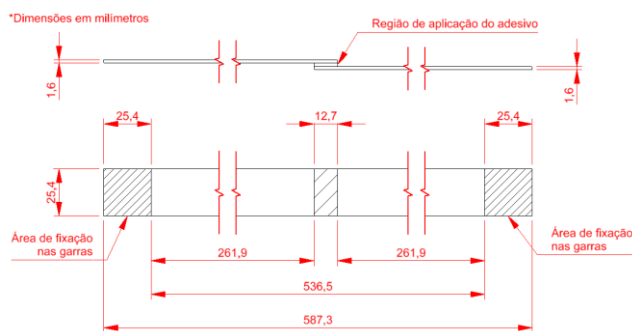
Método de união e dimensional dos corpos de prova. (Elaborado pelo autor)
